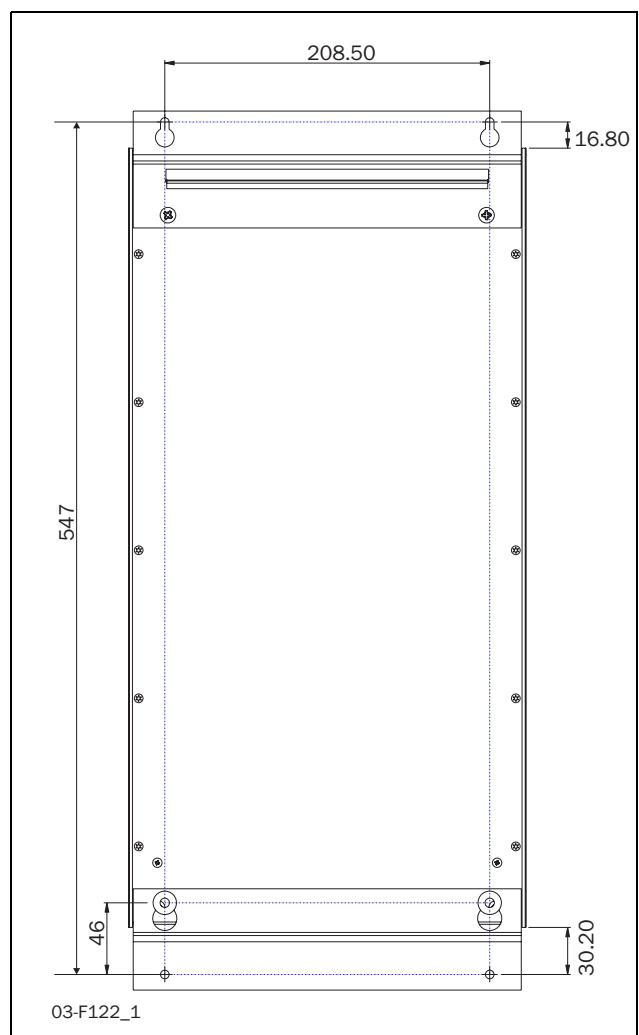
Dima dei fori per softstarter da MSF-170 a MSF-250 con staffa di montaggio superiore invece di guida DIN.
